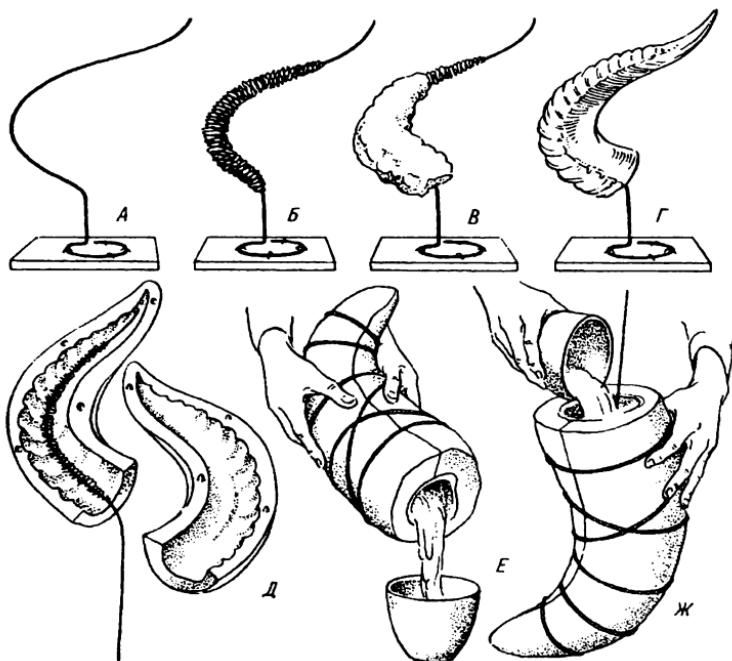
Изготовление искусственного рога: А – металлическая арматура рога; Б – арматура с укрепленной металлической сеткой (каркас рога); В – начало лепки пластилином; Г – вылепленный рог; Д – гипсовая форма рога в два куска; Е – выливание гипса из формы для удаления воздушных пузырьков; Ж – установка металлической арматуры для рога и заливка формы жидким гипсом
